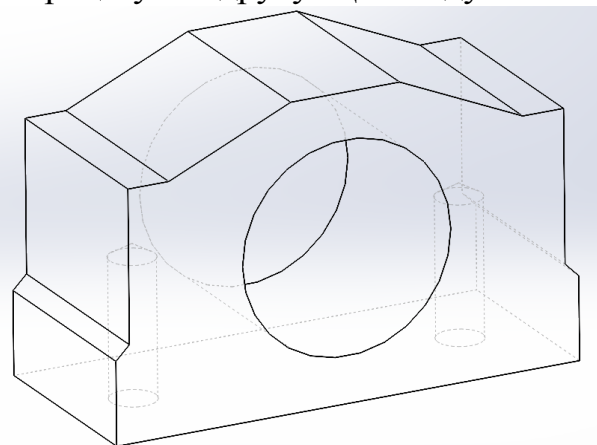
САД-модель тестового зразку деталі «Корпус підшипника».
